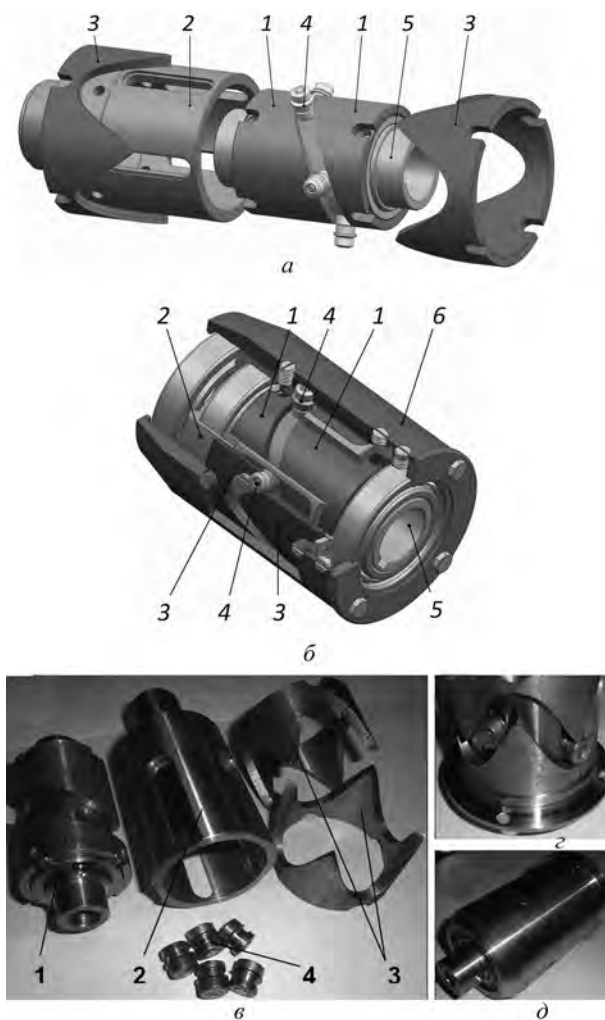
Передача с промежуточными телами качения: модели основных элементов (а), общий вид редуктора (б), основные элементы передачи (в), редуцирующий узел в сборе (г), редуктор в сборе (д): 1 – составной внутренний кулачок; 2 – сепаратор (ведомый вал); 3 – составной наружный кулачок; 4 – ролики; 5 – ведущий вал; 6 – корпус
